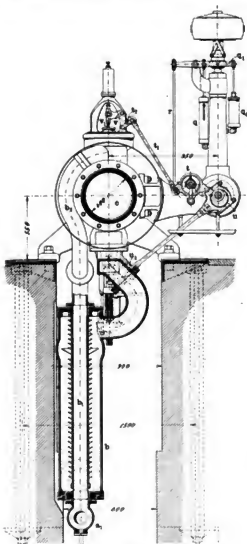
Z. A.: Horizontal-Dampf-Tandem-Maschine.
